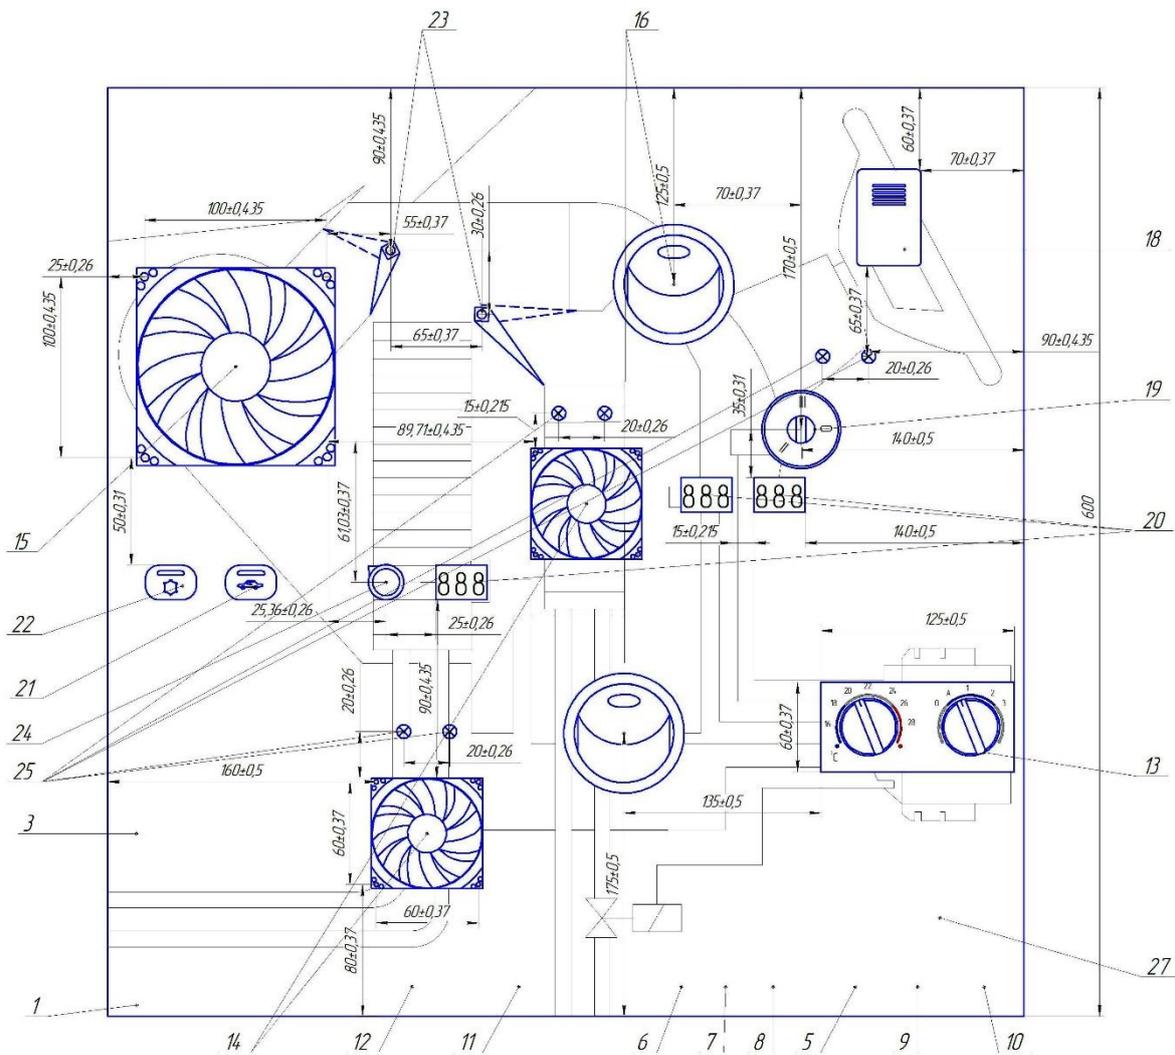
Общий вид стенда «Климатическая установка автомобиля»
